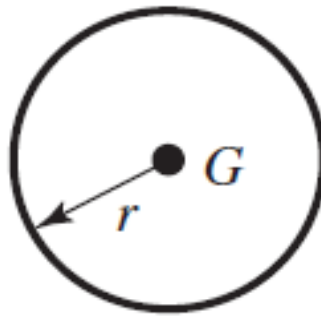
18: PATRÓN DE SOLDADURA DEL SOPORTE PARA ACTUADOR. FUENTE: AUTOR.
